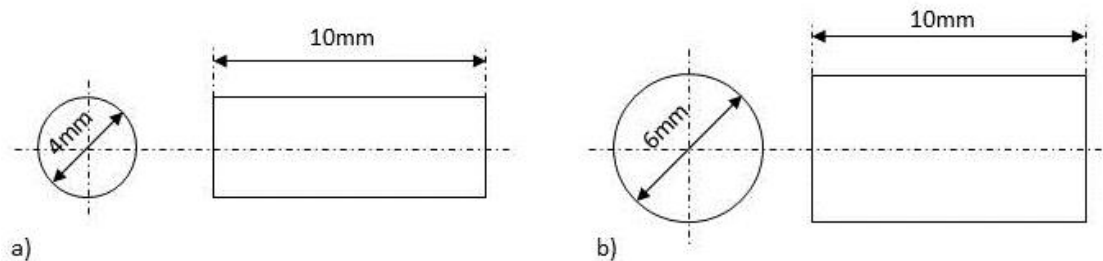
Abmessungen und Geometrie der Dilatometerproben a) RN9VNb, b) RN22VNb.
